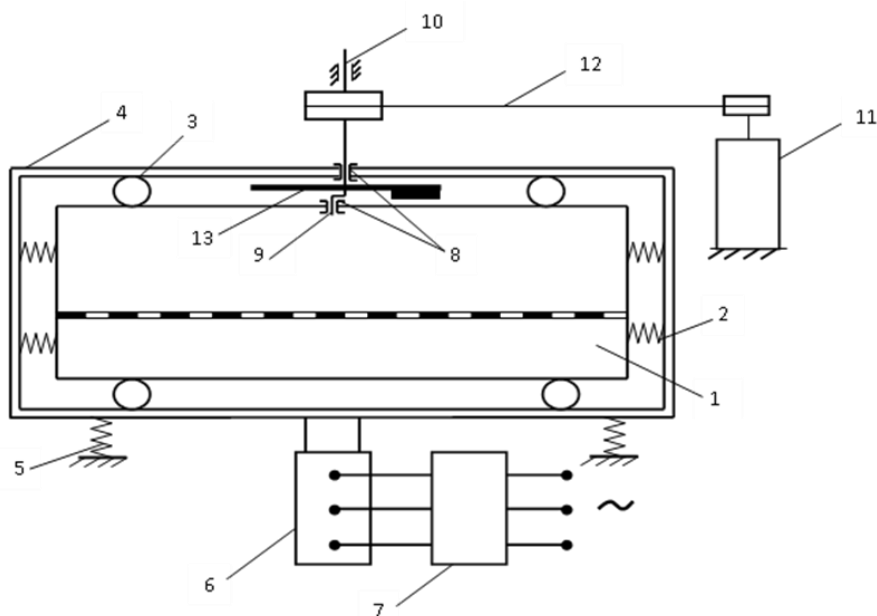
Схема вибрационного грохота с пространственной траекторией колебаний сита: 1 – корпус просеивающей поверхностью; 2 – упругие элементы; 3 – кинематические пары; 4 – подвижная рама, совершающая вертикальные колебания; 5 – амортизаторы; 6 – вибропривод вертикальных колебаний; 7 – преобразователь частоты; 8 – скользящие пары; 9 – кривошип, обеспечивающий горизонтальные круговые колебания корпуса с ситом в подвижной раме; 10 – вертикальный вал; 11 – электродвигатель; 12 – ременная передача; 13 – маховик с грузом, уравнивающий силы инерции корпуса.
